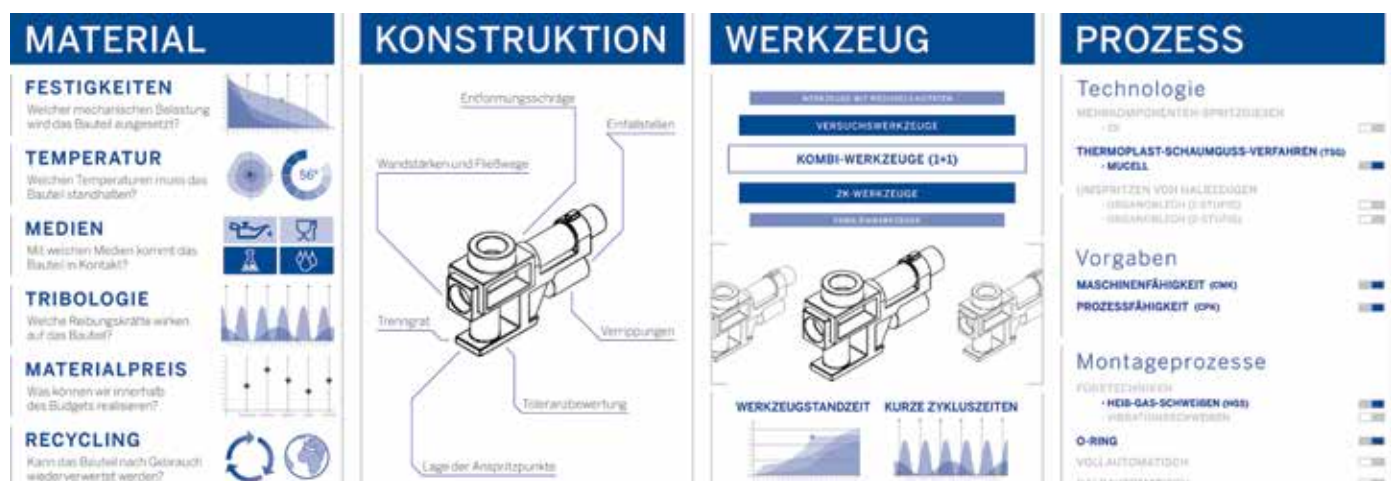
Optimale Auslegung von Material, Design, Werkzeug und Prozessen mithilfe des Quick Checks (Bild: Pöppelmann K-TECH)
